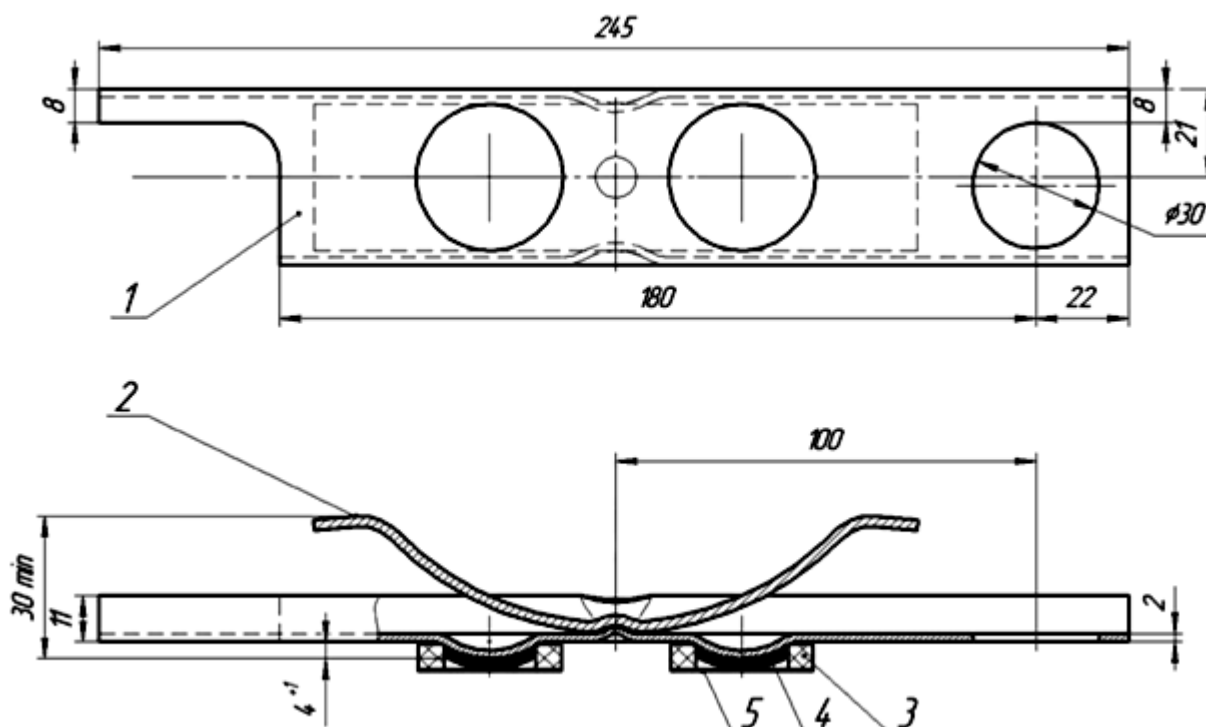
Соединитель рельсовый стыковой пружинный (мм).
